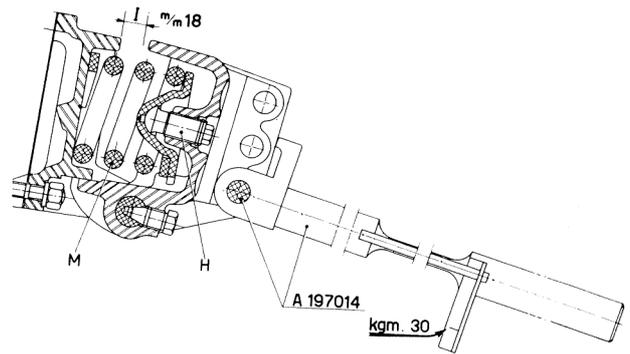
Section sur le support du dispositif d'attelage des outils.
